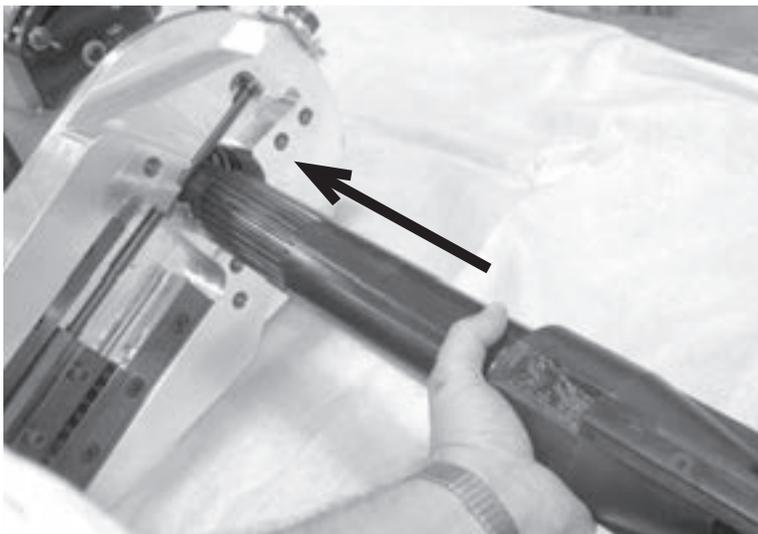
Inserte el mandril a través del carro portaherramientas de punta única.
